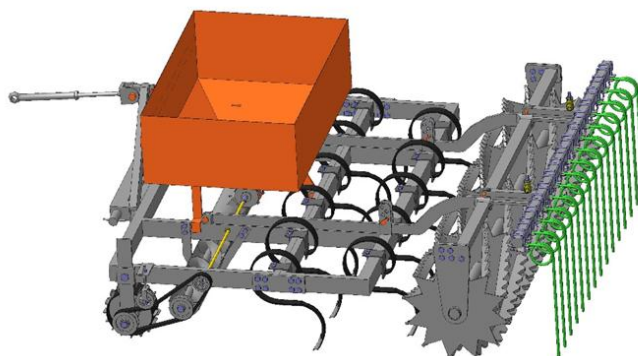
3D модель комбинированного почвообрабатывающего агрегата с внесением удобрений
